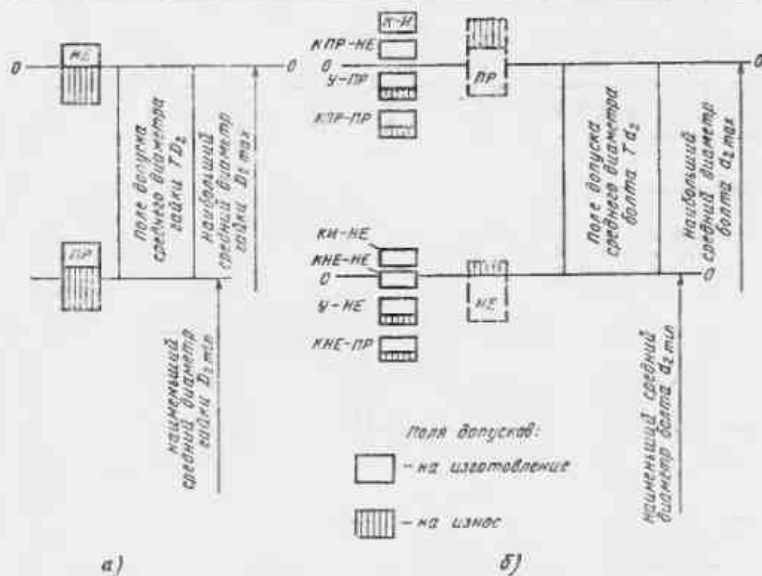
Схема расположения полей допусков среднего диаметра резьбы калибров для проверки: а — гайки; б — болтов
